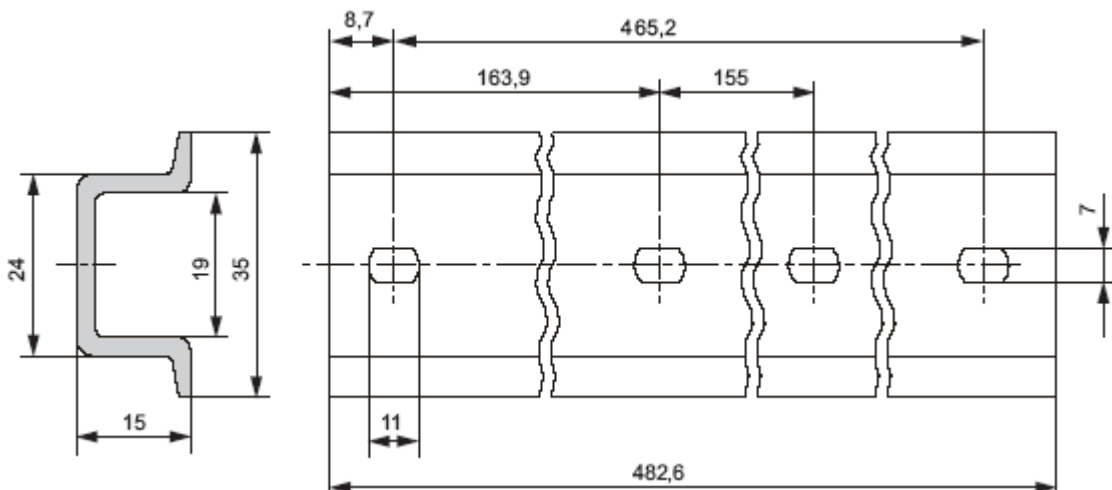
Габаритный чертеж 483-миллиметровой стандартной профильной шины
